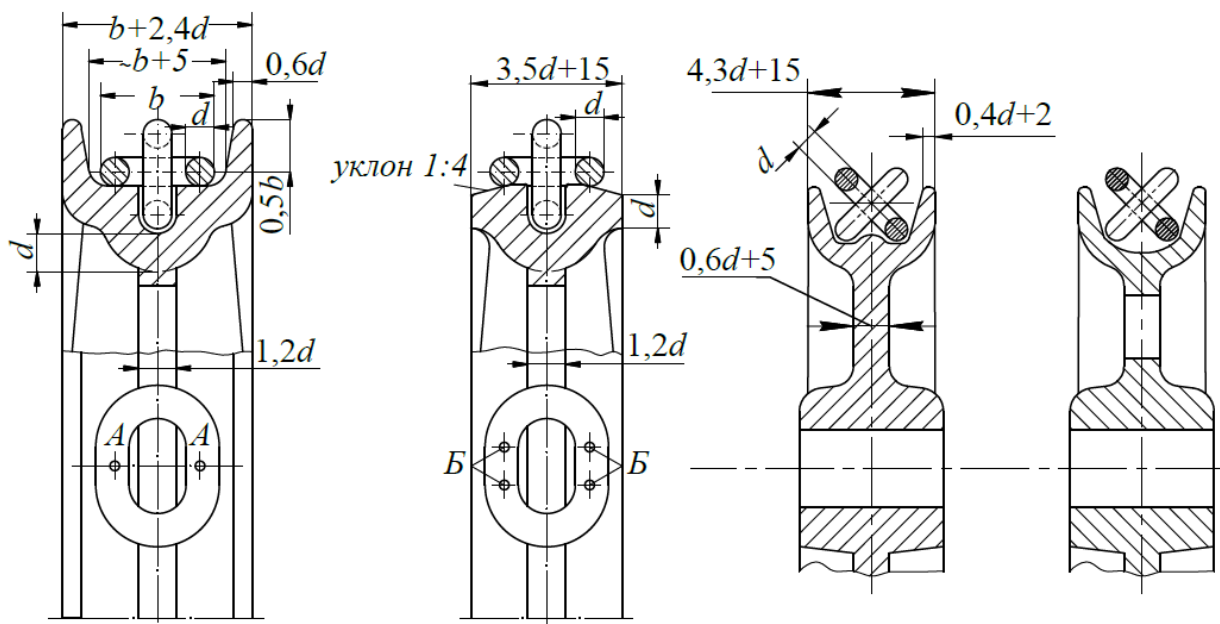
Профиль ручья блоков для сварных цепей
